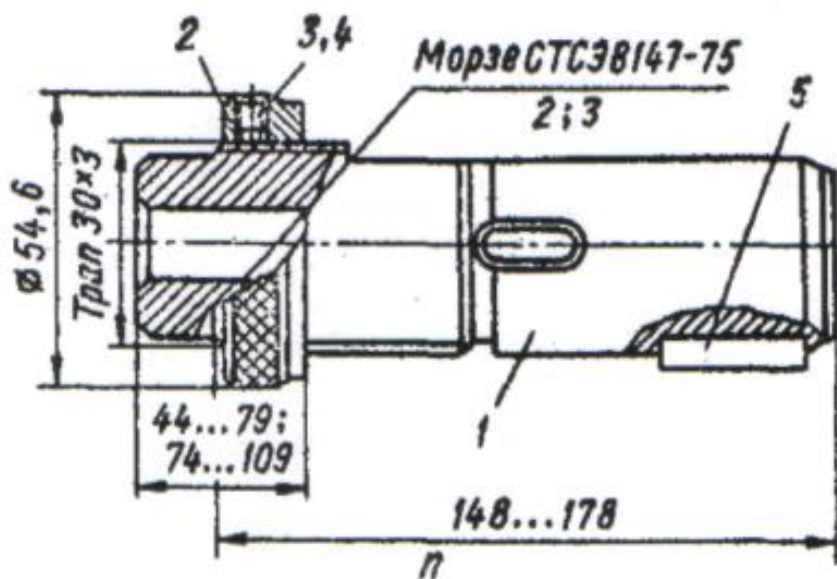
Регулируемая оправка для станков с ЧПУ
